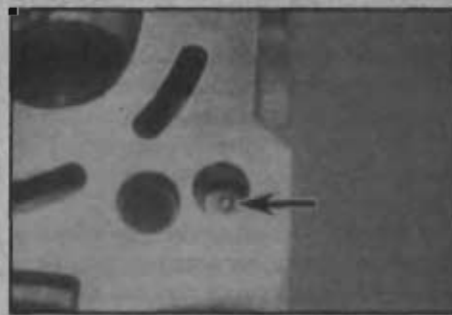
Расположение обратного клапана в отверстии головки цилиндров для подачи масла к распределительным валам
